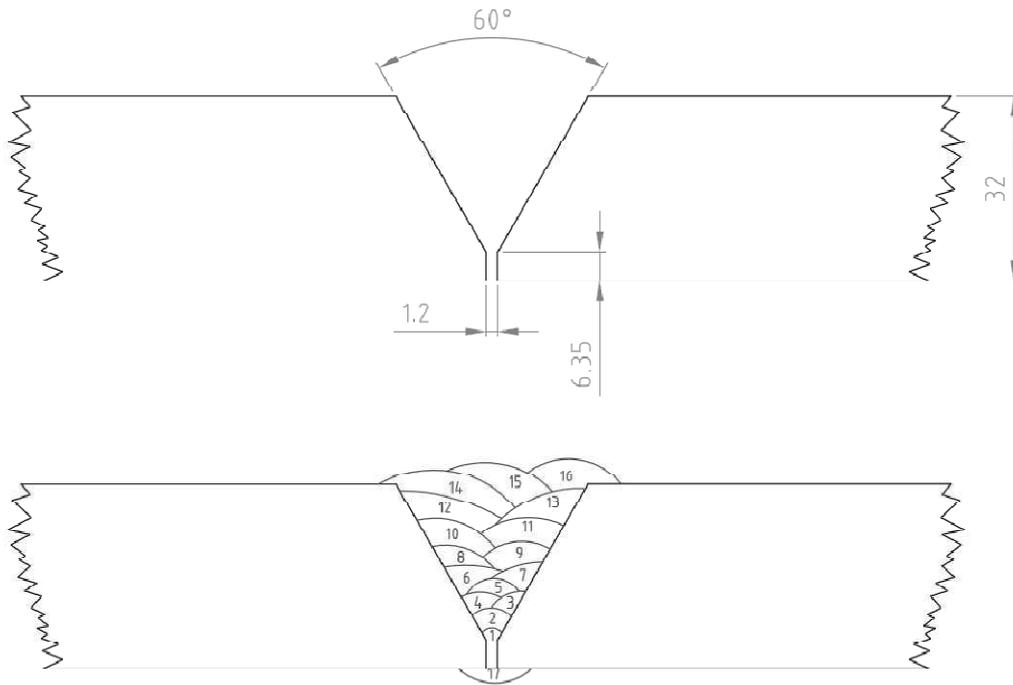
1 Diseño de Junta y Número de Pases de Soldadura
